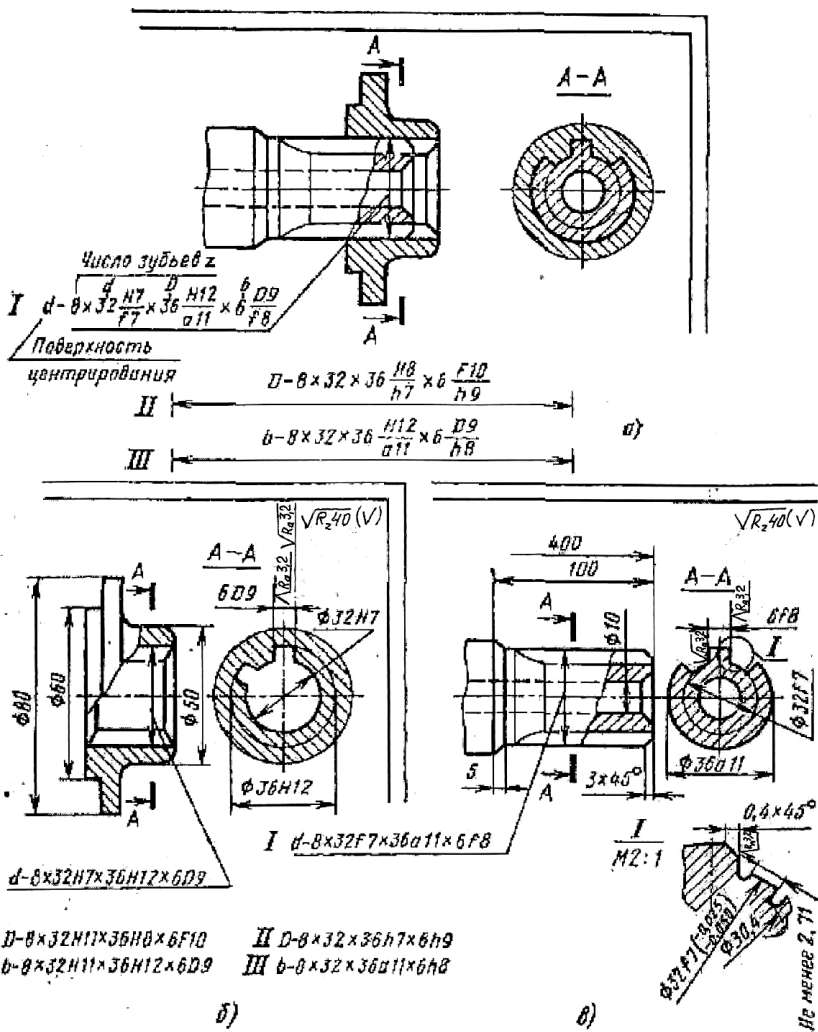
Обозначение допусков и посадок прямого шлицевого соединения на сборочном чертеже (а) и на рабочих чертежах деталей (б и в); варианты обозначения при центрировании:
